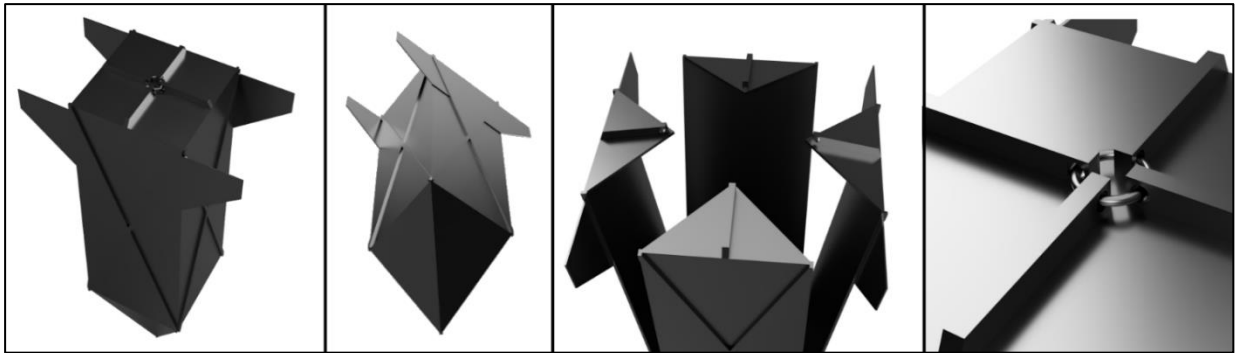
Cofre de cuatro lados. De izquierda a derecha: Vista superior cerrada, vista inferior cerrada, vista superior abierta, y vista en detalle de la brida en la parte superior.
